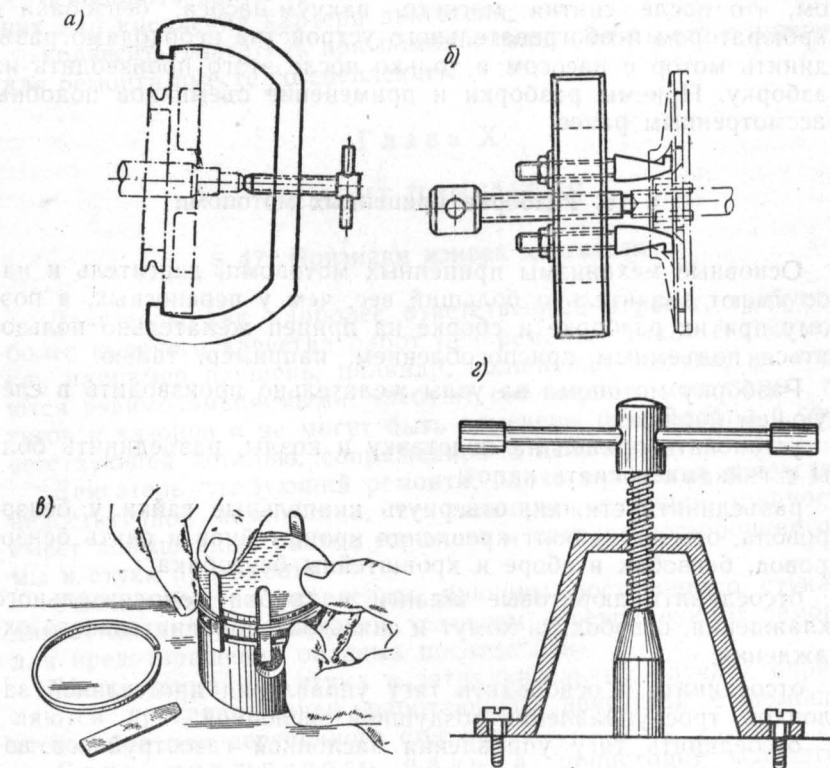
, а — съемник для снятия маховика у мотопомп М-600 и СМ-2; б — съемник для снятия рабочего колеса мотопомп М-600 и СМ-2; в — снятие и надевание поршневых колец на поршни при помощи пластинок; з — съемник для снятия картера двигателя с цапфы вала.
